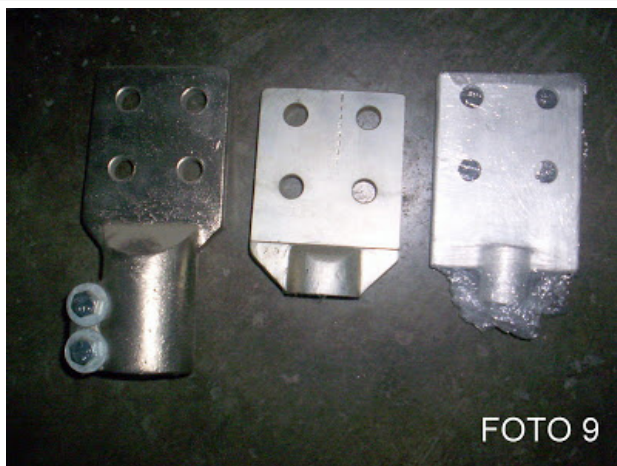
Se muestran boquillas para baja tensión tipo espada.
